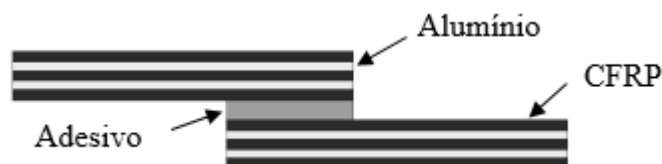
Configuração da junta CFRP-AL-CFRP-AL-CFRP, com um comprimento de sobreposição de 12,5 mm.
